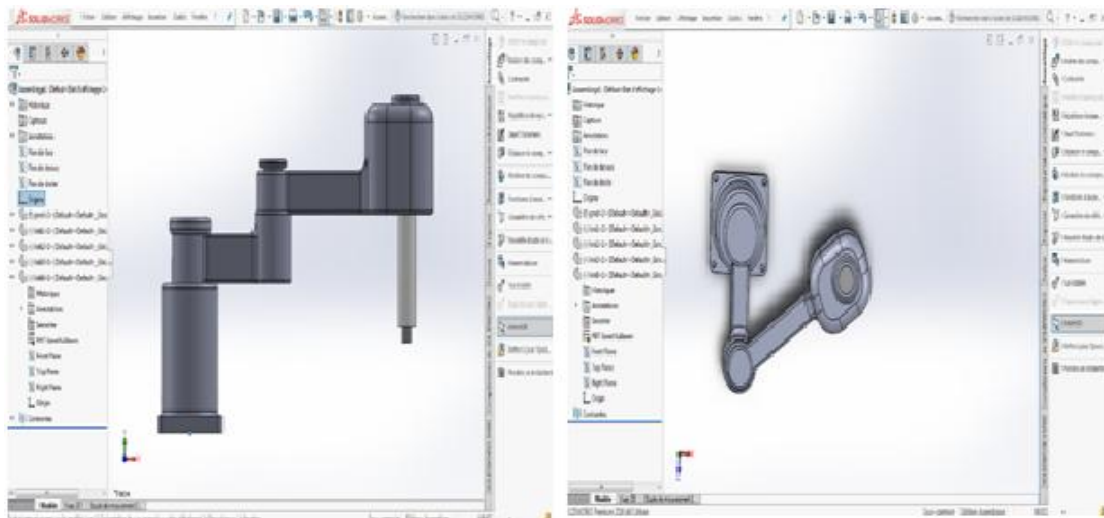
Vue d'ensemble du robot 1 et 3
